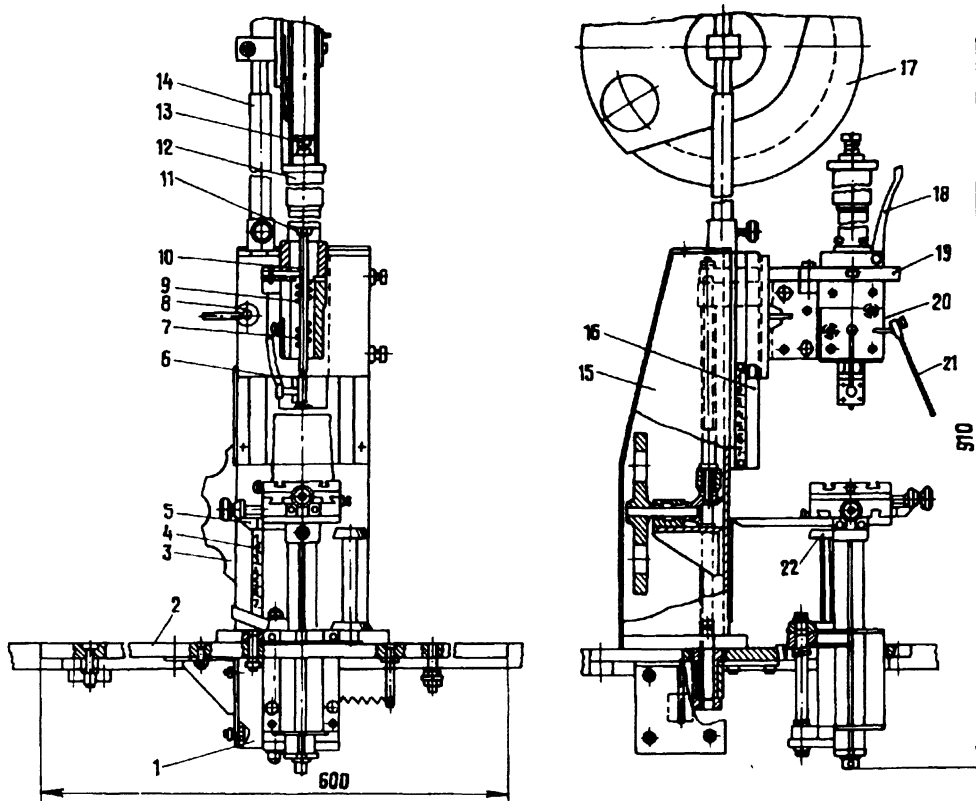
Головка машины K543 для приварки проволоки к детали с развитой поверхностью
